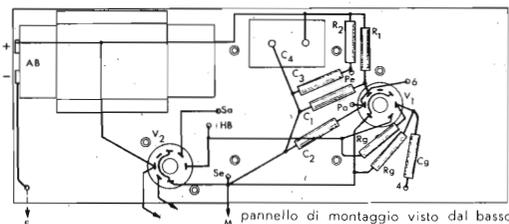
Montaggio e collegamento del ricevitore a due valvole.
